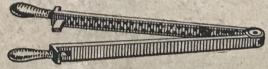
Moule pour fabriquer dragée coulée au moule.
